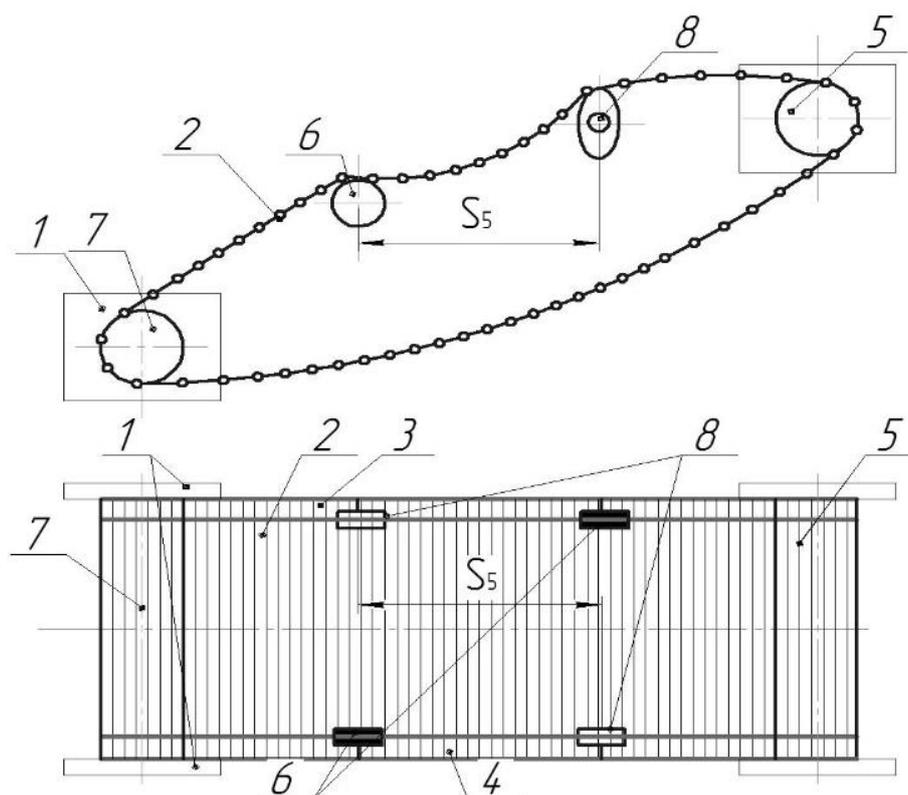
Схема пруткового элеватора с асимметричным расположением встряхивателей машины для уборки картофеля: 1 – рама; 2 – элеватор прутковый; 3, 4 – ветви пруткового элеватора; 5 – ролики ведущие; 6 – ролики поддерживающие; 7 – ролики ведомые; 8 – эллиптические встряхиватели
